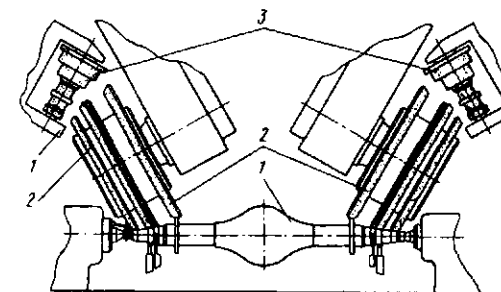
Схема совмещенного двустороннего шлифования цапф заднего моста автомобиля ЗИЛ-130: 1 – обрабатываемая деталь; 2 – шлифовальные круги на шпинделе станка; 3 – алмазный правящий ролик
